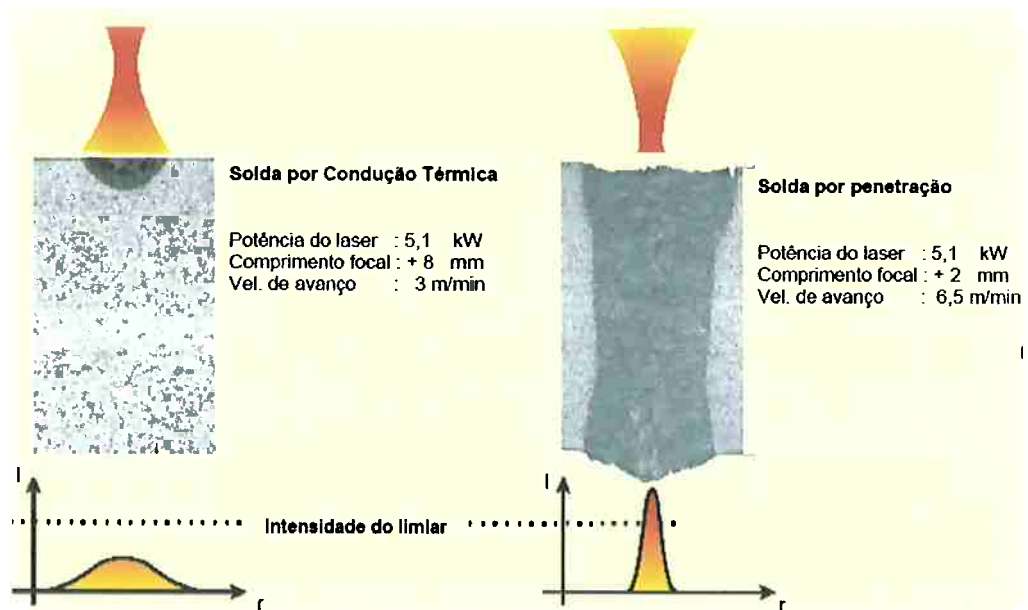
Soldagem a laser por condução térmica e soldagem a laser profunda (Batalha – 2003)
